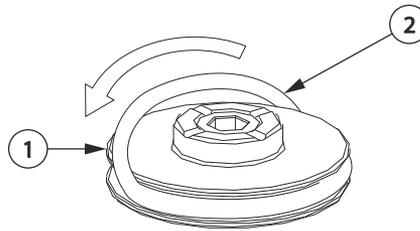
Einsetzen der inneren O-Ring-Dichtung
